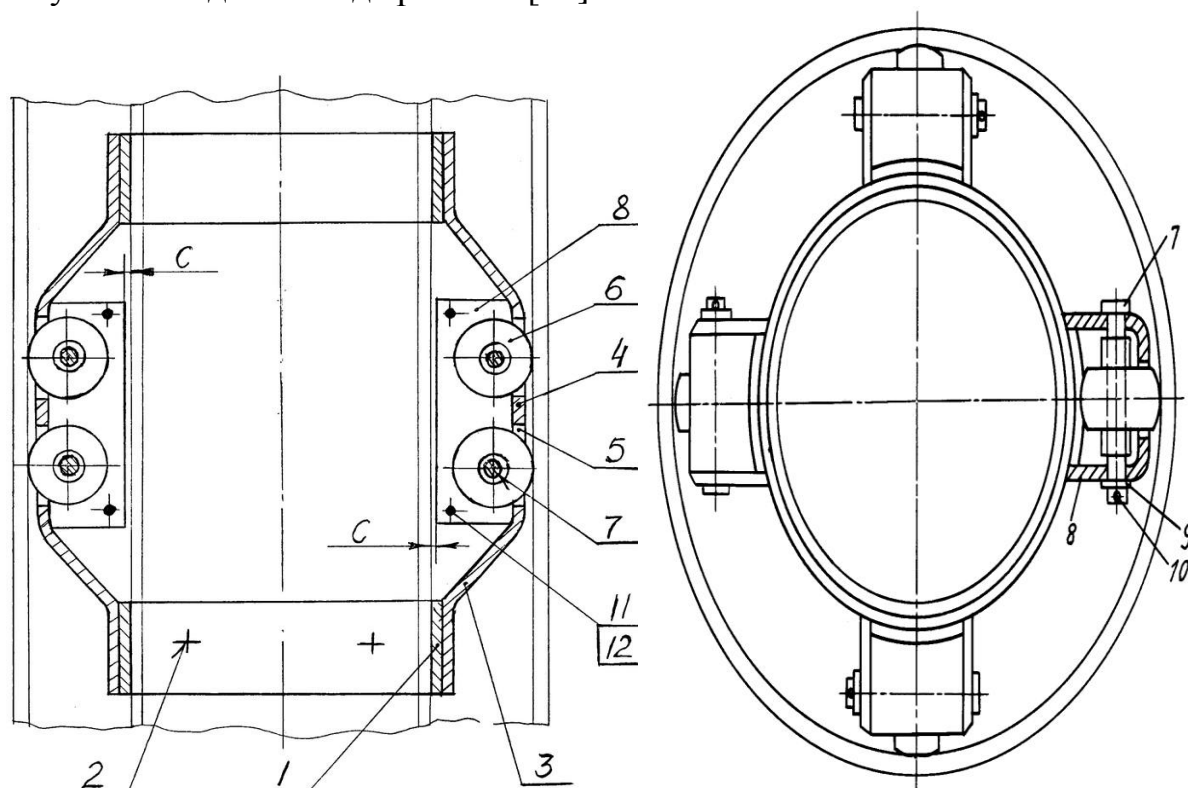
Центратор : 1-установочные кольца -, 2 - резьбовые отверстия, 3 - упругие планки, 4 – короб, 5- пазы, 6 – ролики, 7 – оси роликов, 8 – борты короба, 9 – шайбы, 10 – шпинты, 11 – заклепки, 12 – распорные втулки.
